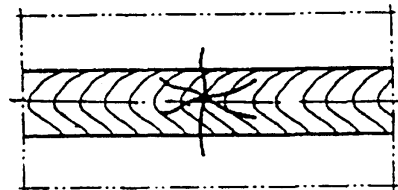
Радиальные трещины сварного соединения
